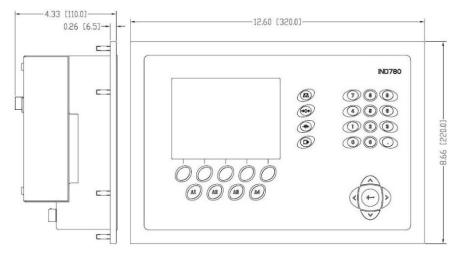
Dimensões do gabinete do IND780 para montagem em painel
